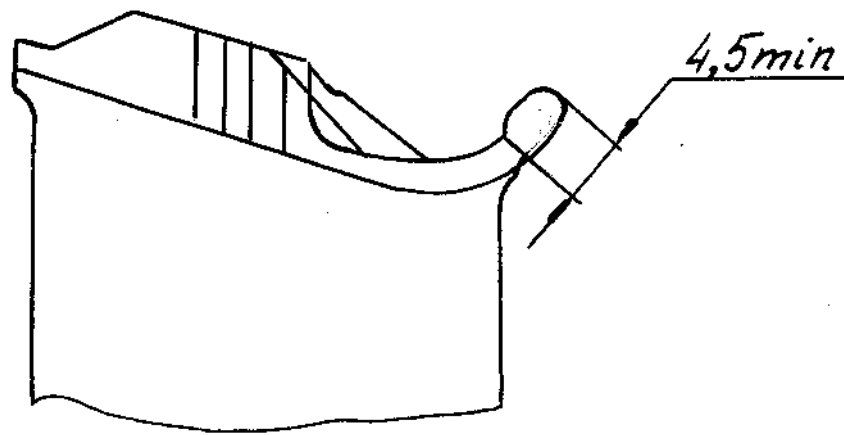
Схема наплавлення лабіринтового гребінця лопатки
